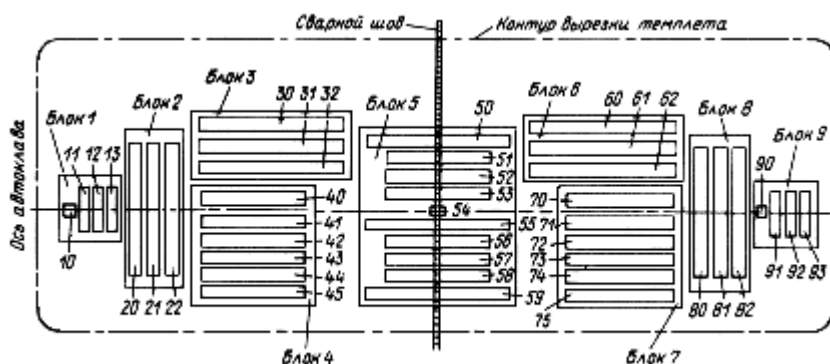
Схема расположения на темплете блоков заготовок образцов для испытания металла автоклава
